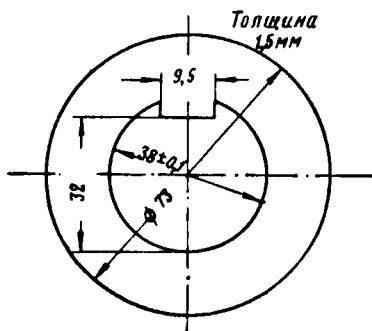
Крепежная шайба вентилятора делителя напряжения ДК-601
